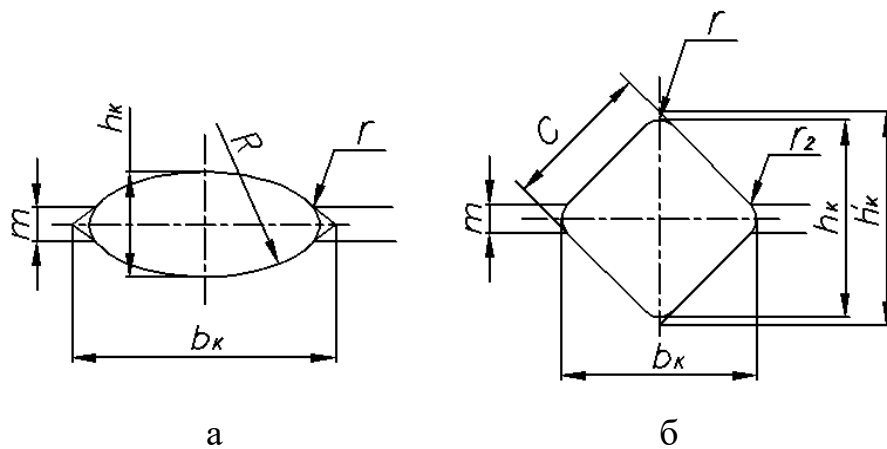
Основні параметри калібрів для вальцювання заготовок: овальний (а) та квадратний (б)
